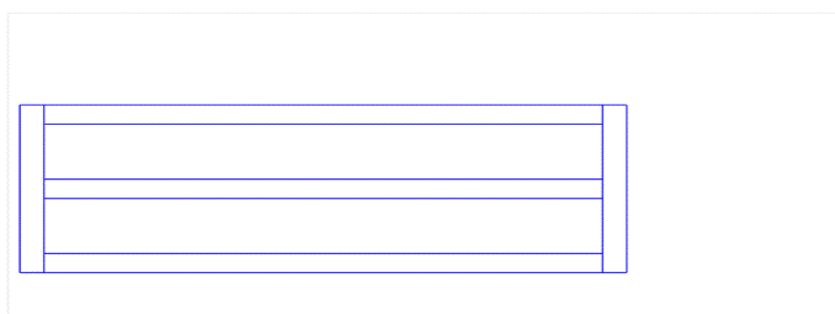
Схема конструкции кондуктора (первый вариант)
